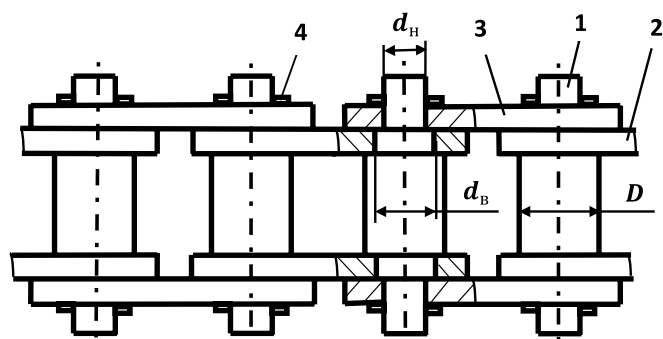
Фрагмент приводной пластинчатой цепи [10] со ступенчатыми валиками
